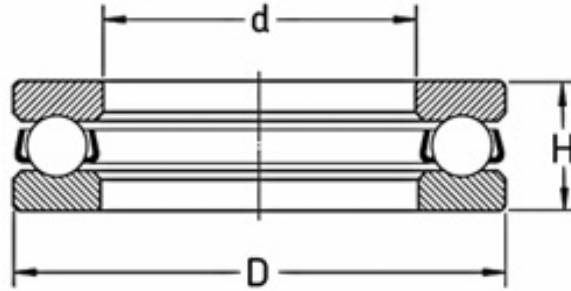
Rodamiento axial. Fuente: Autoría Propia
